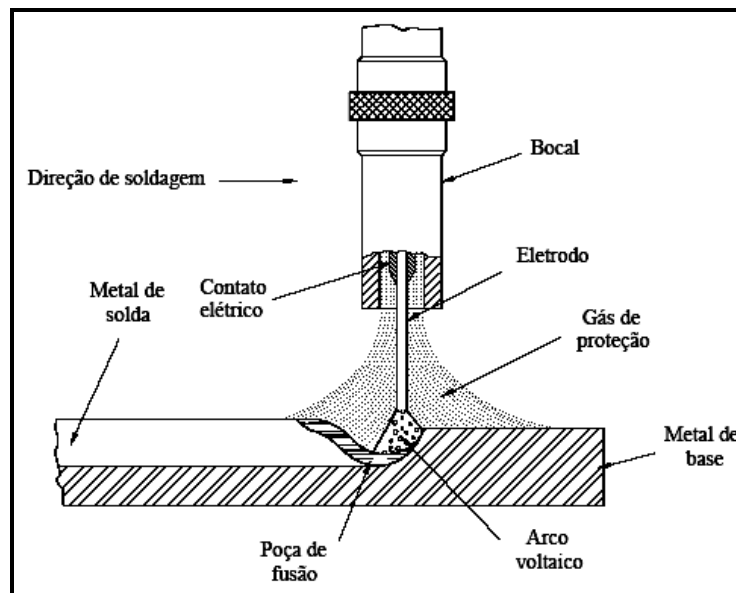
Detalhe da soldagem GMAW (MIRANDA e FERRARESI, 1999).
